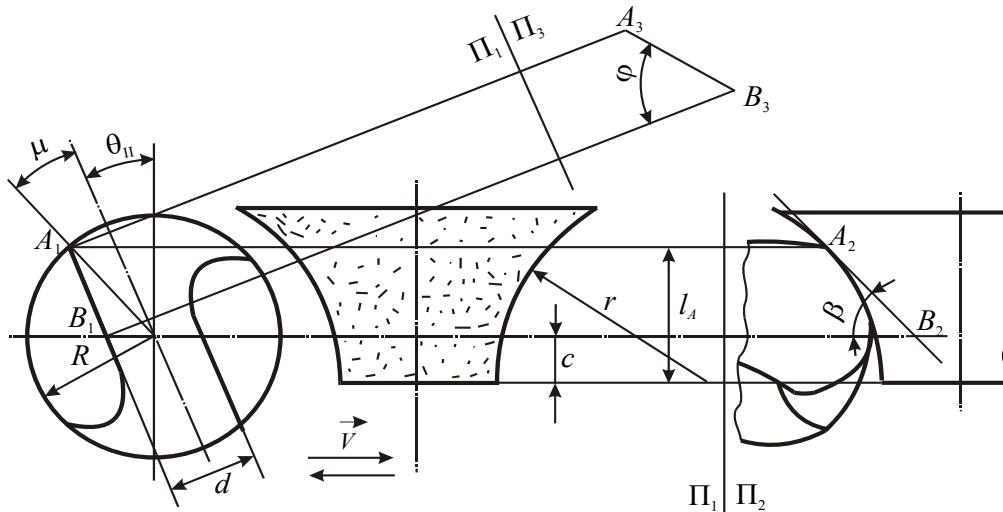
Схема заточки задних поверхностей сверла фасонным шлифовальным кругом
